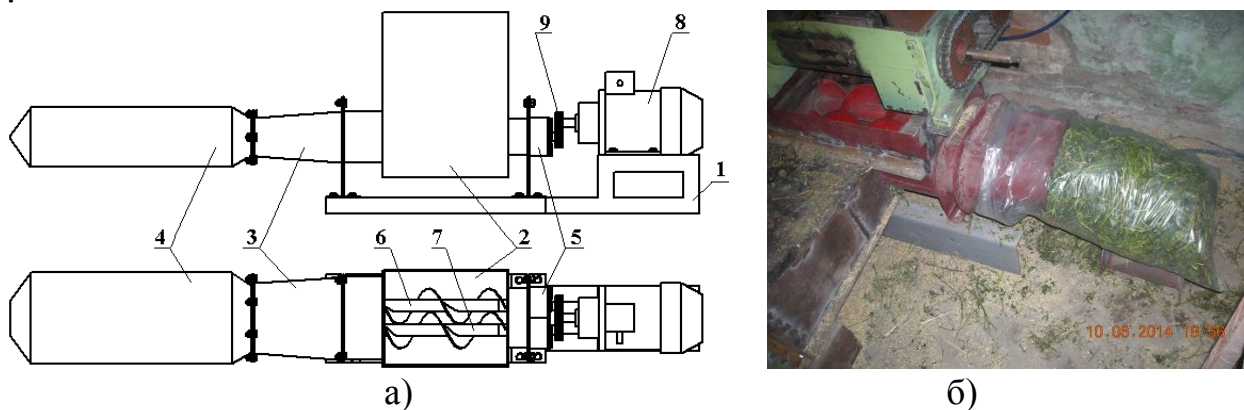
Конструктивна схема а) та фото лабораторної установки б) двошнекового ущільнювача рослинної сировини: 1 - рама; 2 - бункер; 3 - дифузора; 4 - рамка з поліетиленовою (поліпропіленовою) валізою; 5 - підшипниковий вузол; 6, 7 - гвинти; 8 - електричний мотор-редуктор; 9 - ланцюгова передача
